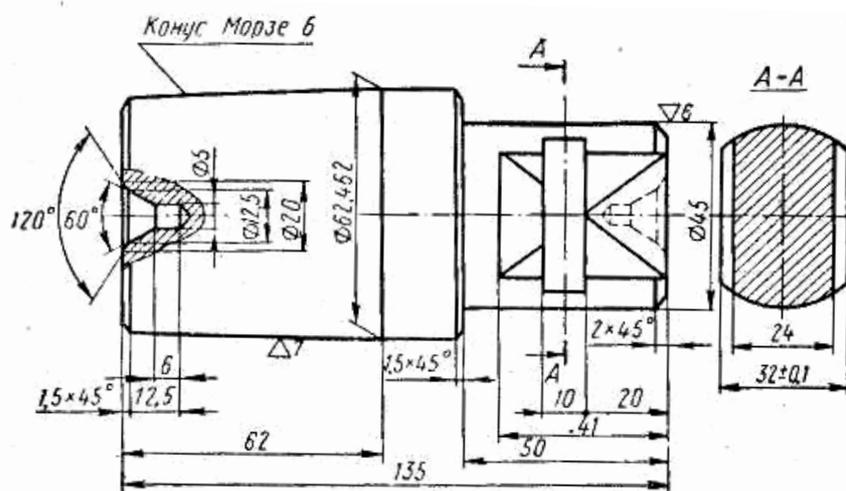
Шпиндель токарного станка (рабочий чертеж)
